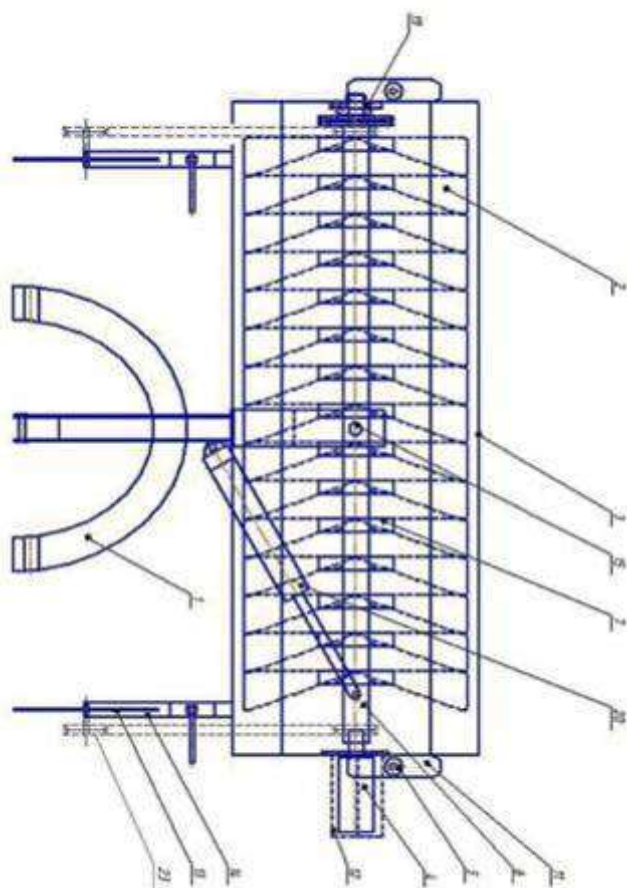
Ротационный рыхлитель (вид сверху):
